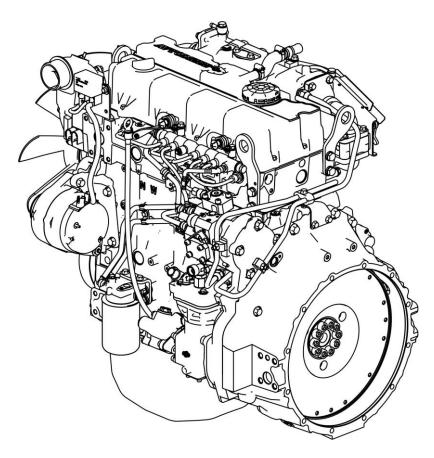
а – Двигатель ЯМЗ-53443-21 (общий вид слева)
